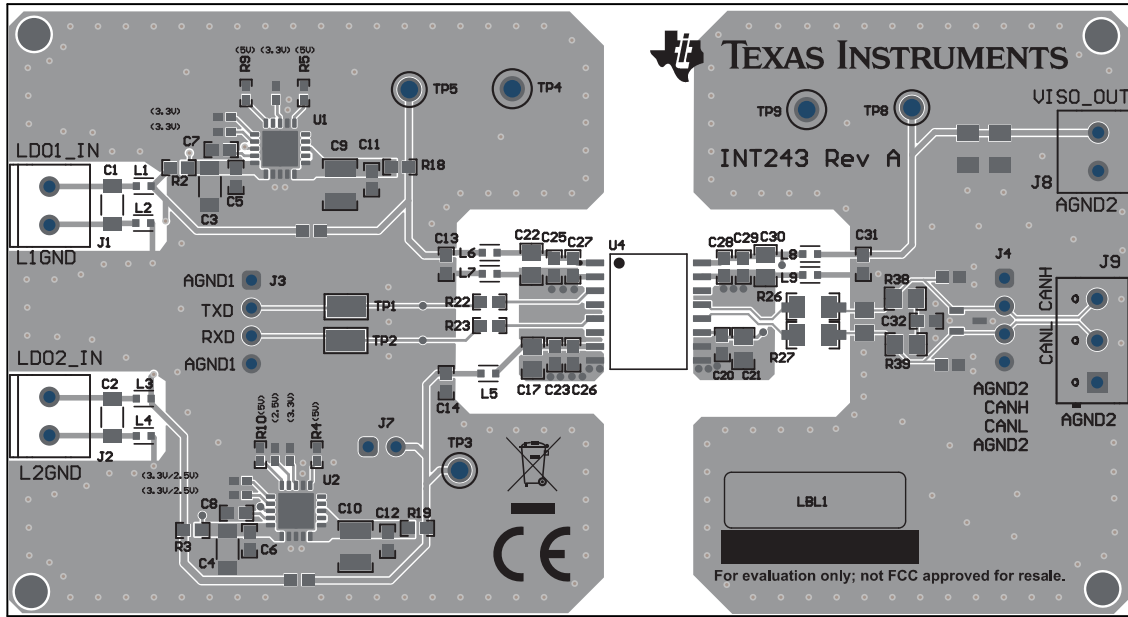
ISOW1050DWEEVM PCB 布局 - 顶层
